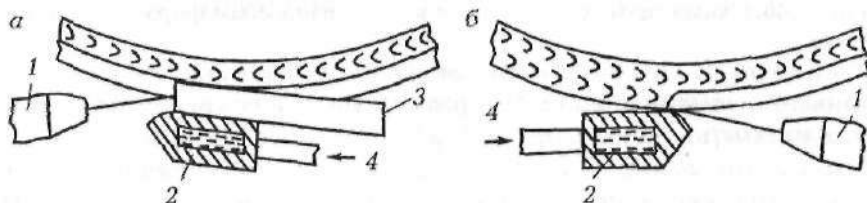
Схема начала сварки с принудительным формированием шва:
